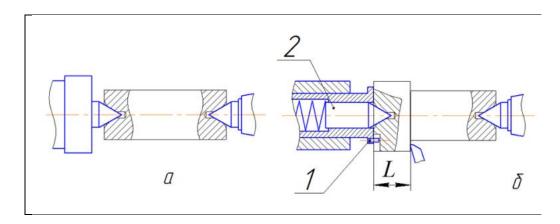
Схема установки заготовок по центровым отверстиям: а – установка в жестких центрах; б – установка с плавающим центром
